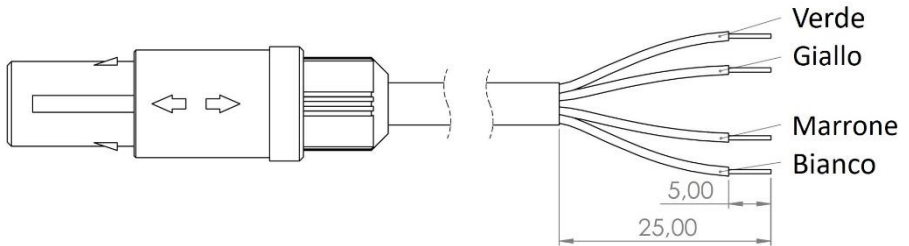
Collegamento elettrico dei cavi allo strumento di misura
